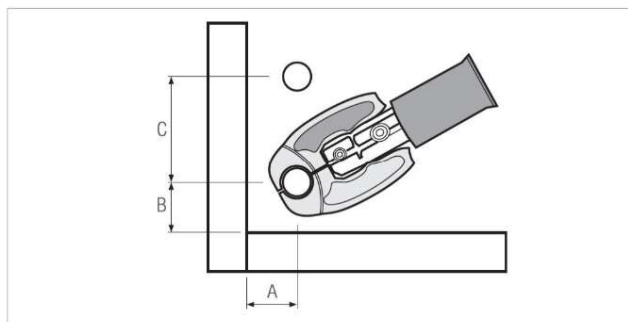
Distanța minimă de presare perete-pardoseală
